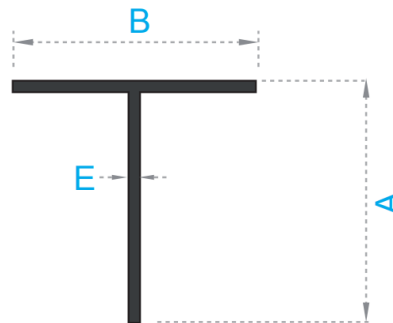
Dimensiones perfil T aluminio Cedal. Fuente: CEDAL [46].
